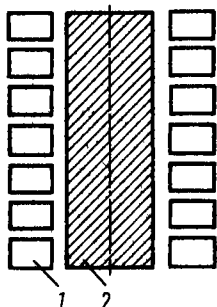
Индуктор для закалки цилиндрических деталей:
